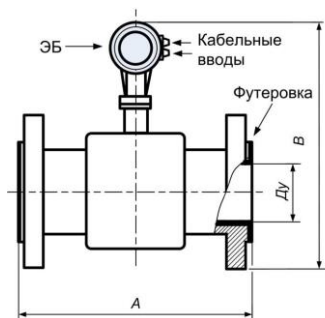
Вид конструкции сенсора с установленным ЭБ
